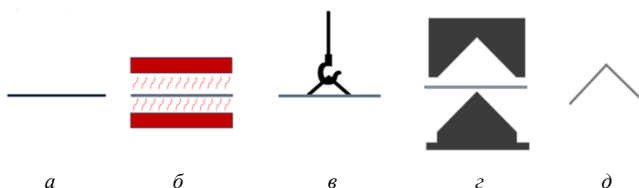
Схема технологического процесса термоштамповки термопластов: а – сырой лист термопласта; б – предварительный нагрев листа; в – перенос нагретого листа в пресс; г – штамповка листа; д – готовая деталь
